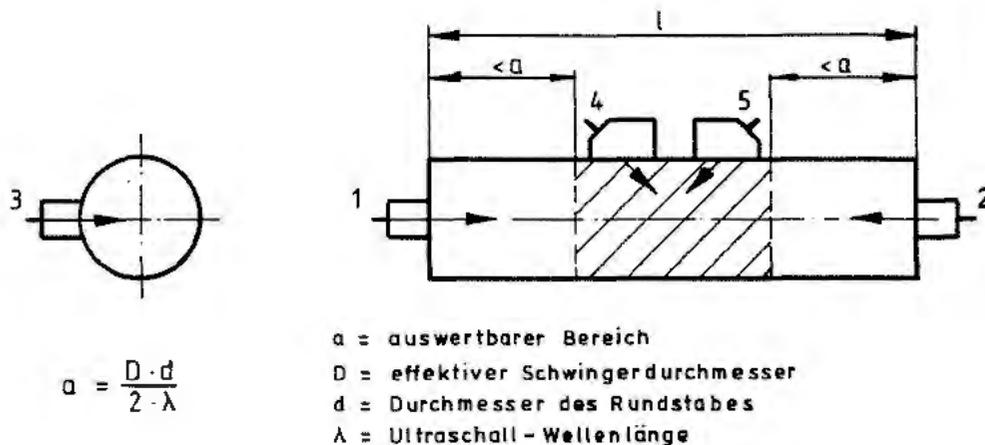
Einschallpositionen bei Rundstäben
